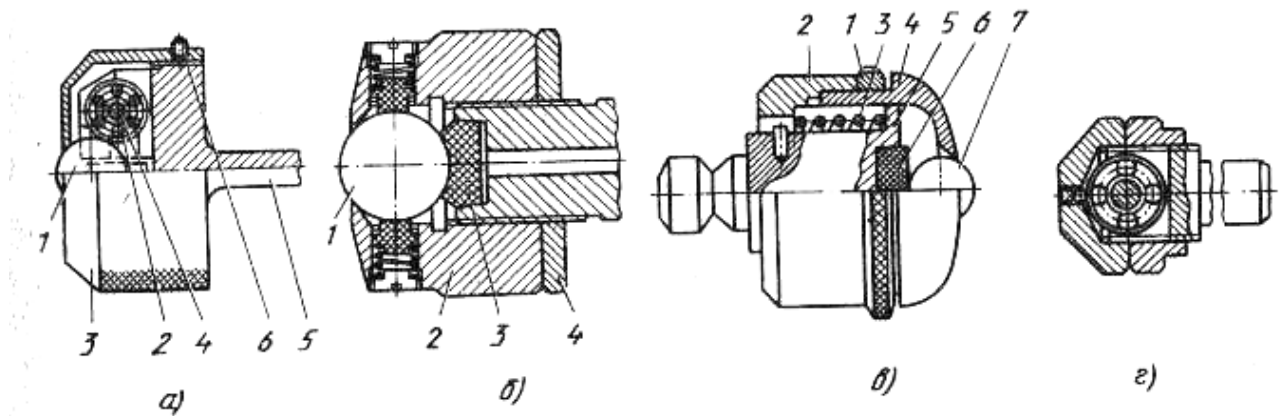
Робочі частини інструментів із кульками для вигладжування зовнішніх поверхонь обертання [30]
